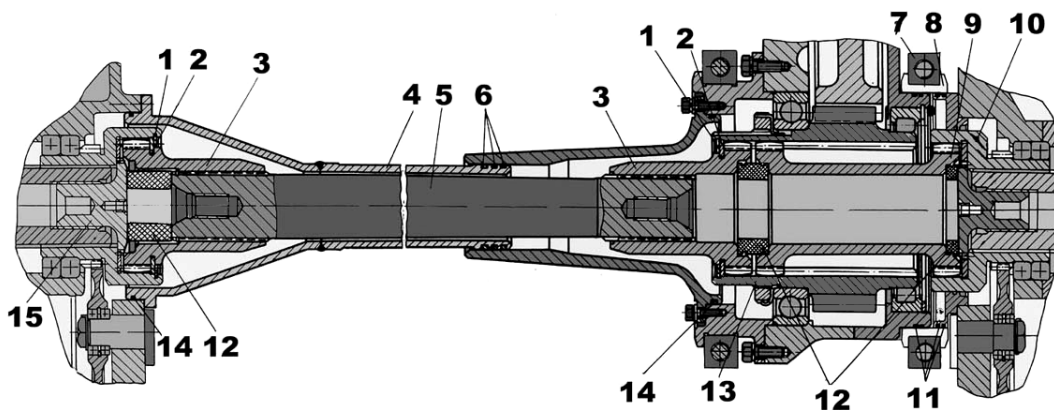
Соединение входного редуктора с правой и левой КП: 1 – стопорные пружинные кольца; 2 – полукольца; 3 – зубчатые муфты; 4 – кожух; 5 – вал; 6 – резиновые кольца; 7 – бугель; 8 – вкладыши; 9 – зубчатая муфта; 10 – ведущая зубчатка правой КП; 11 – резиновые уплотнительные кольца; 12 – резиновые буфера; 13 – ведомая шестерня входного редуктора; 14 – резиновое уплотнительное кольцо; 15 – пробка первичного вала
